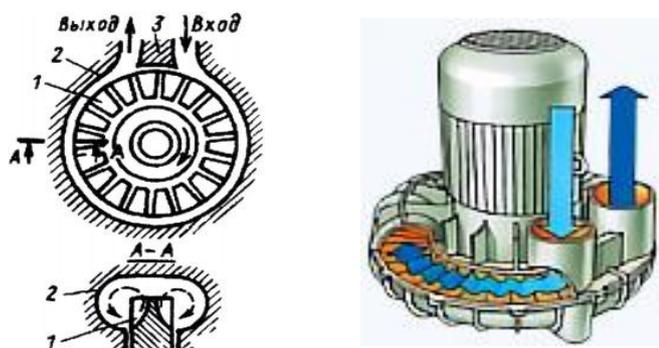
Вихревой насос: 1 – корпус; 2 – рабочее колесо
